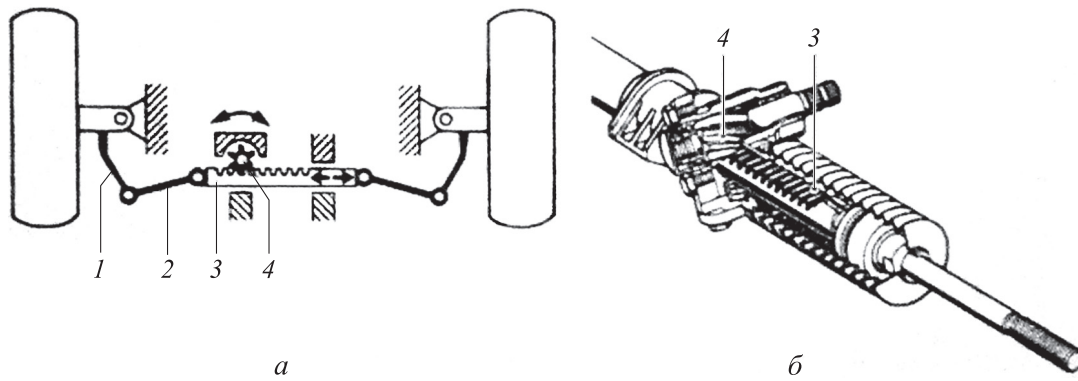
Схема реечного рулевого механизма (а) и его увеличенный фрагмент (б): 1 — рычаг поворотного кулака; 2 — боковая рулевая тяга; 3 — зубчатая рейка; 4 — шестерня
